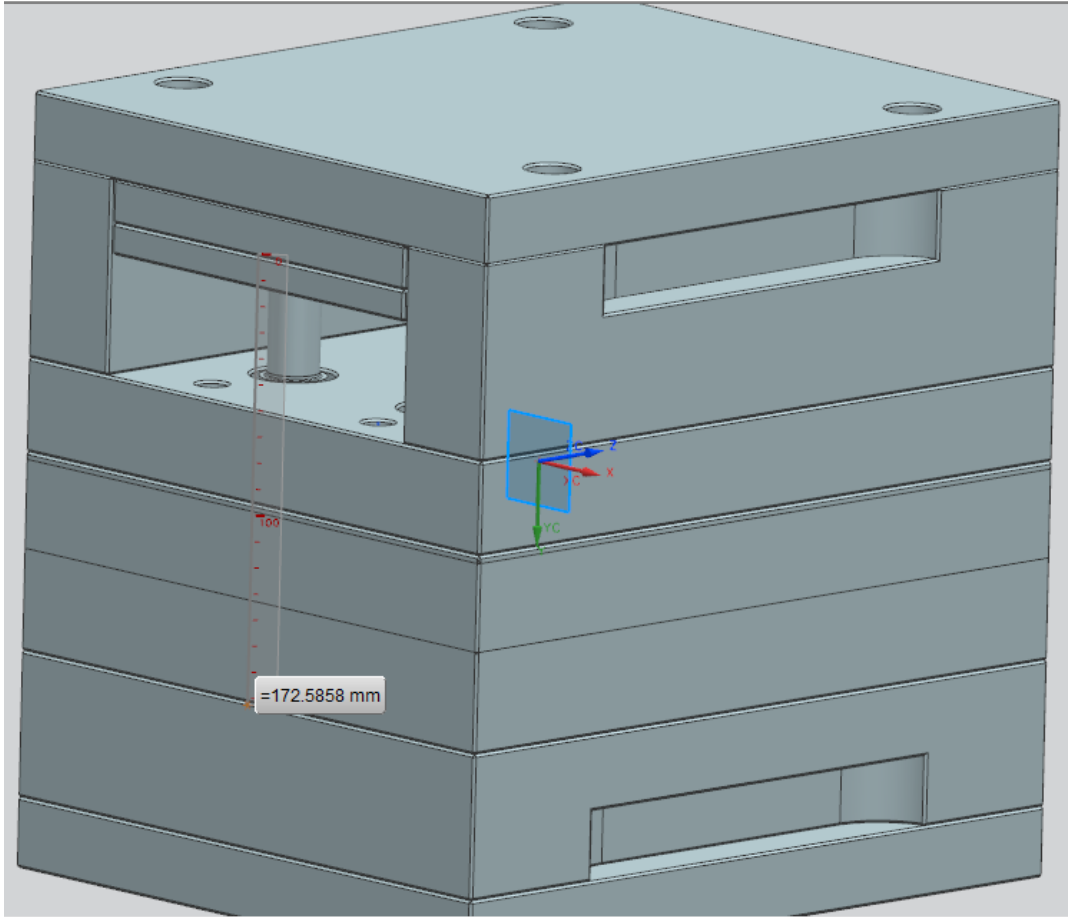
Medición de la longitud en portamolde para perno botador
